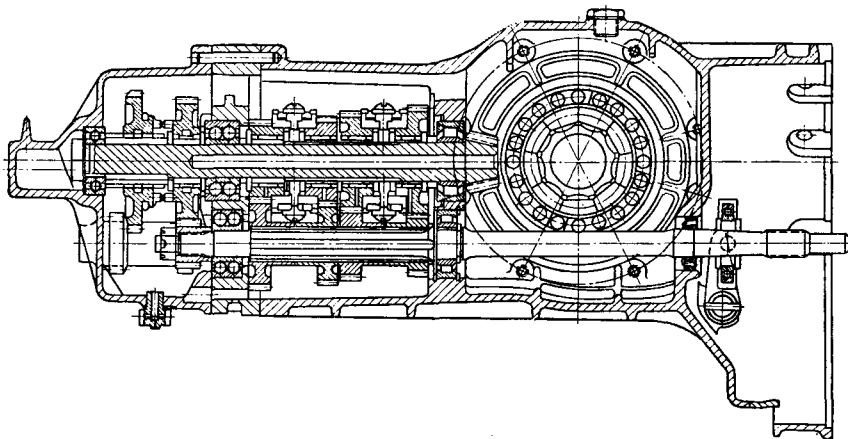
Пятиступенчатая коробка передач спортивного автомобиля Порше (рабочий объем 1,5 л) с задним расположением двигателя.
